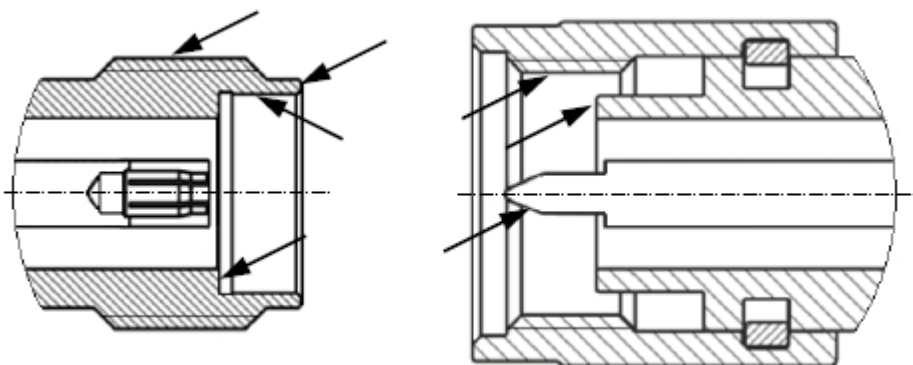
Соединители тип 3,5 мм (розетка слева, вилка справа)
